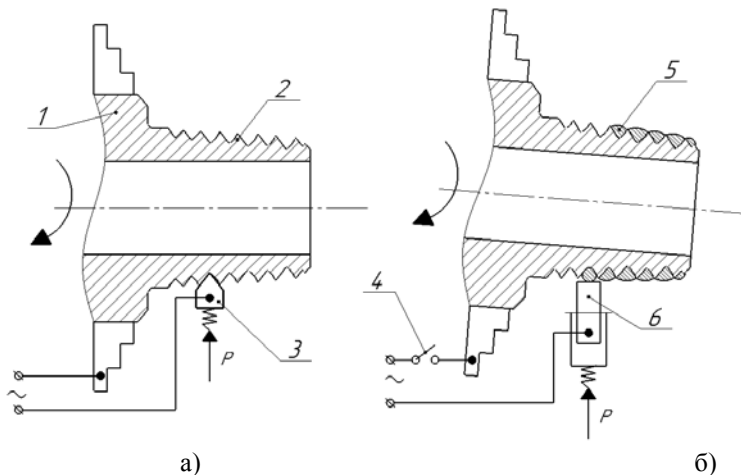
Схемы различных этапов восстановления резьбы замка буровой трубы: а – схема электромеханической высадки; б – схема электроконтактной наплавки; 1 – деталь; 2 – высаженная канавка; 3 – высаживающая пластина; 4 – прерыватель тока; 5 – наплавленный валик присадочного металла; 6 – наплавляющий ролик
